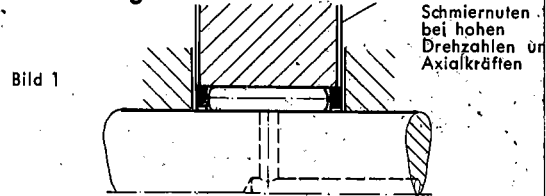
Lagerung für Getriebeäder, Pleuellager, Laufrollen usw. Schmierloch in der entlasteten Zone
